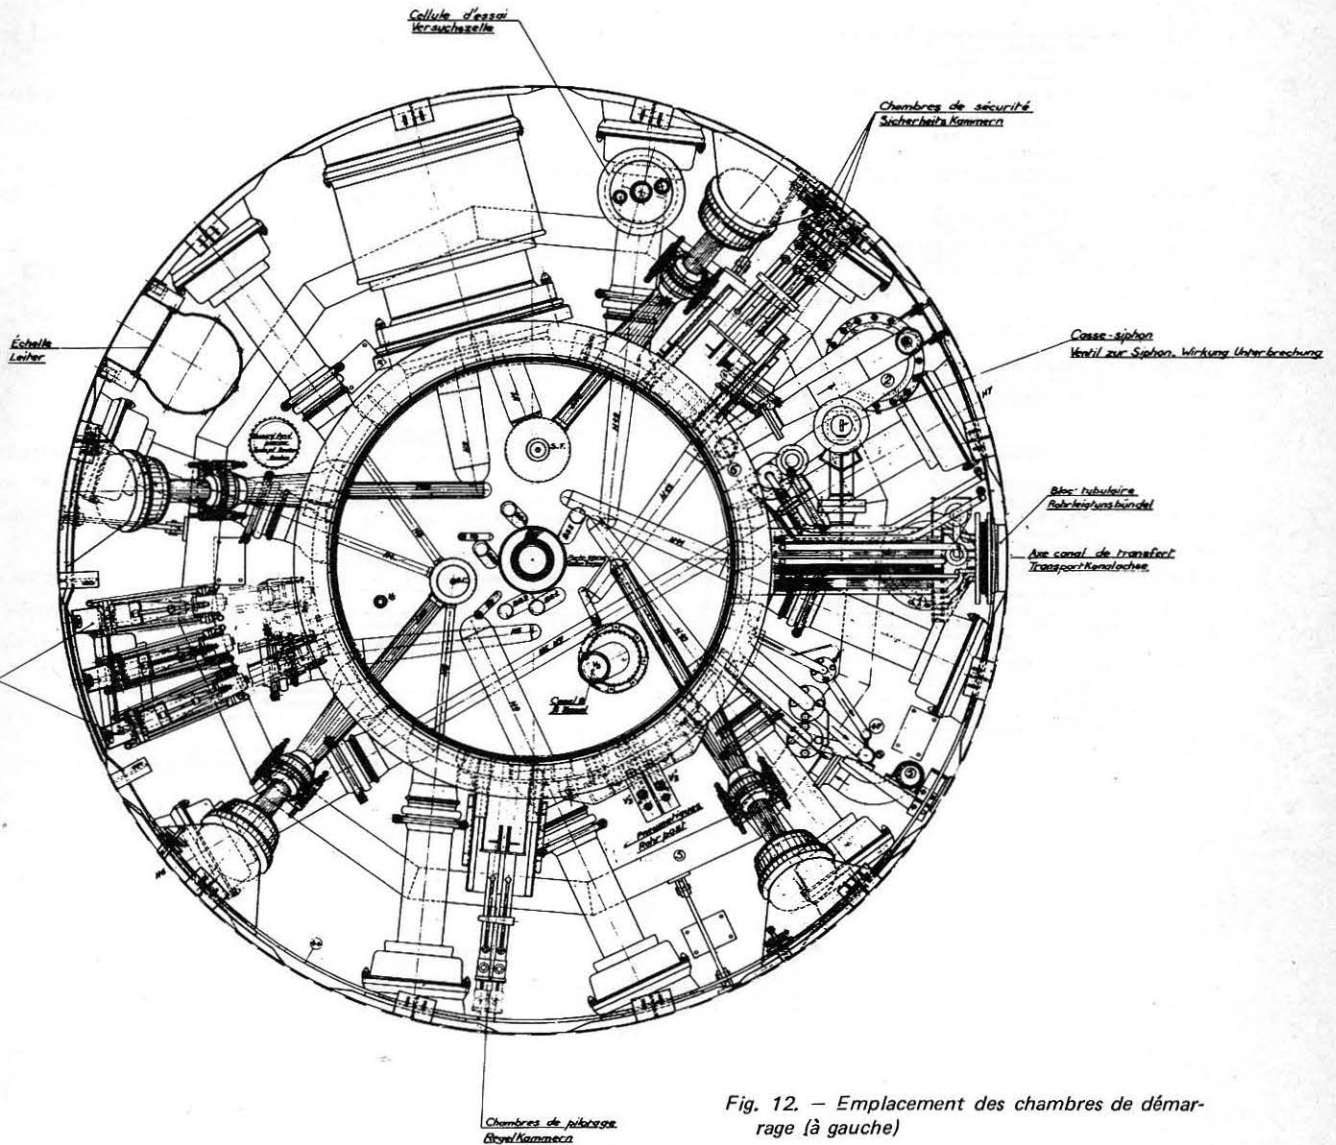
Emplacement des chambres de démarrage (à gauche)
